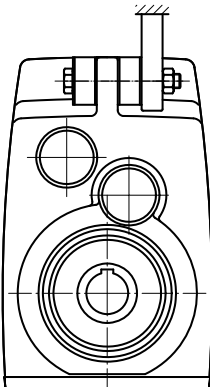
Montage der Gummipuffer (Option G bzw. VG) bei Flachgetrieben
